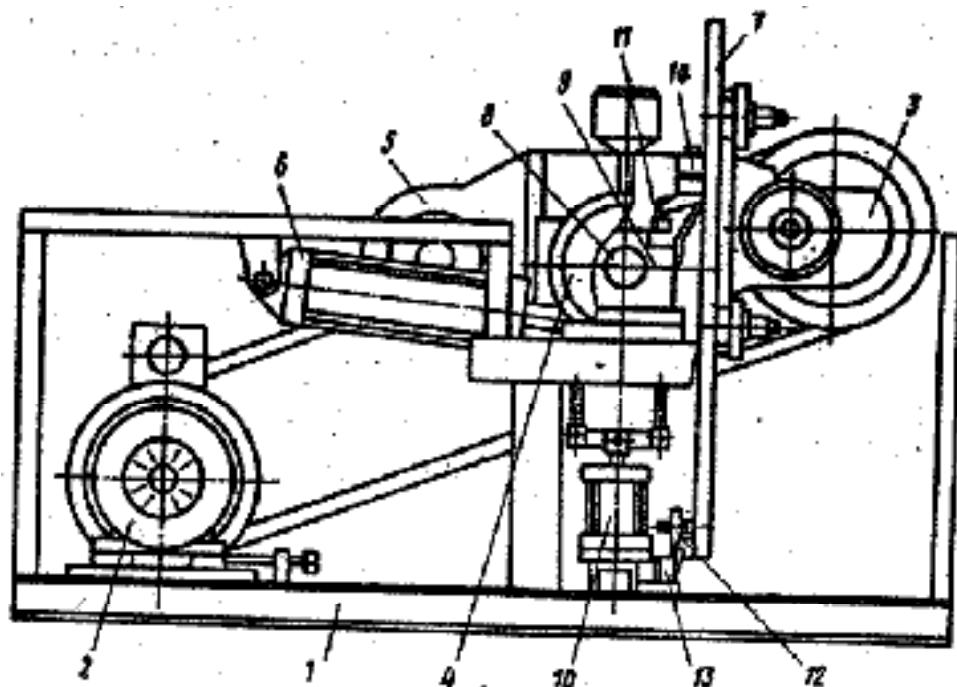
Стенд для испытания и обкатки коробок передач
